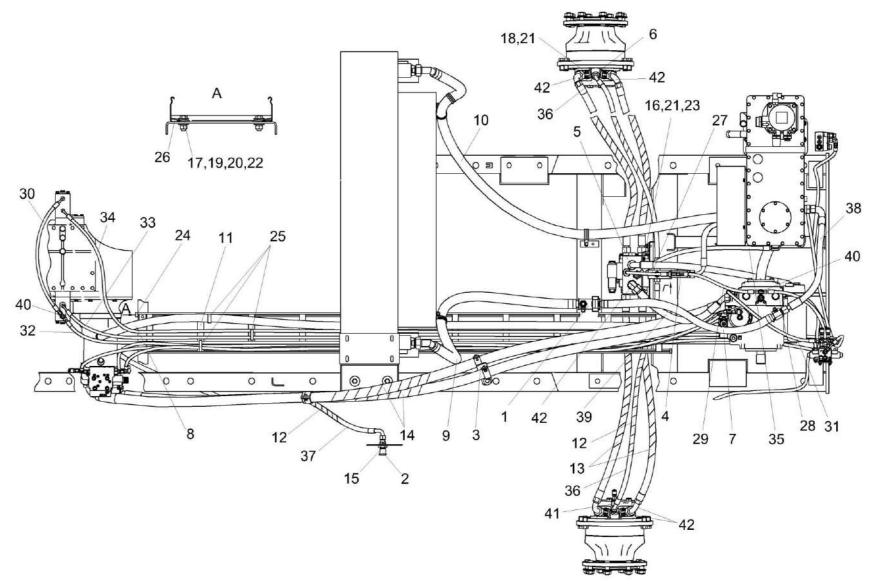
Гидросистема привода ходовой части КВК-2-0601000 (вид сверху)
